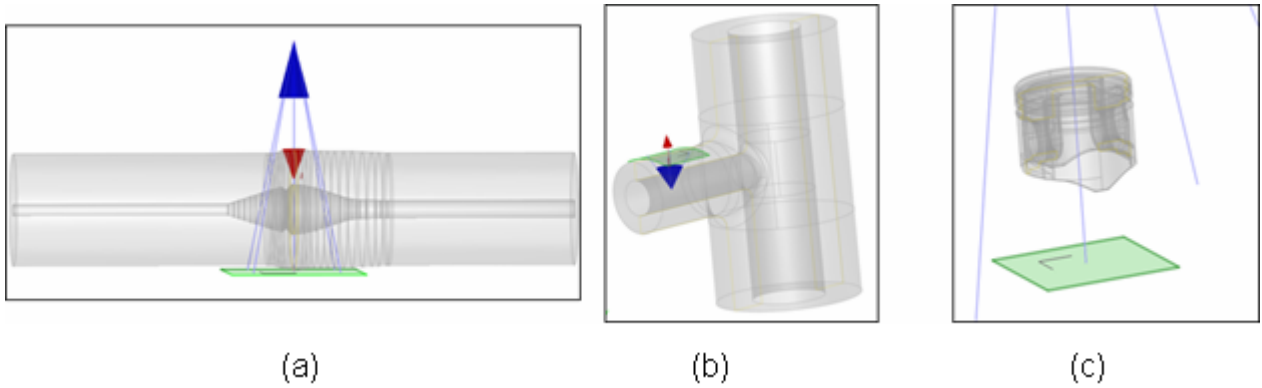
(a) Exemple d'une soudure créée à partir de l'éditeur CAO 2D disponible sous CIVA, (b) exemple d'un objet paramétrique disponible directement dans CIVA, (c) exemple d'une pièce CAO 3D importée par un outil de CAO externe.
